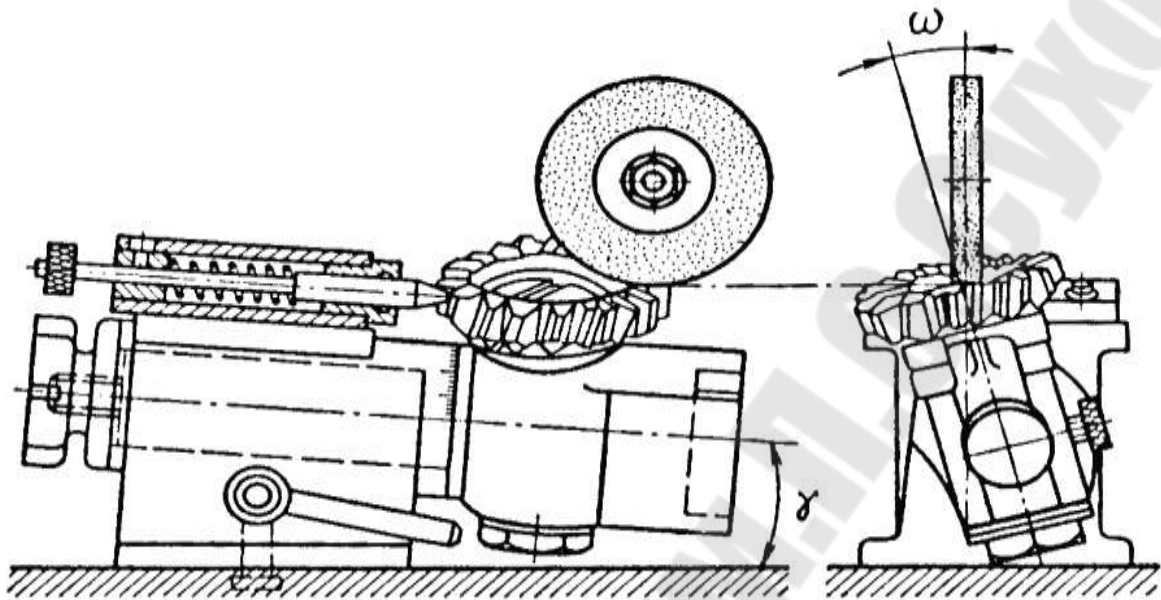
Приспособление для заточки косозубых долбяков на универсально-заточном станке
